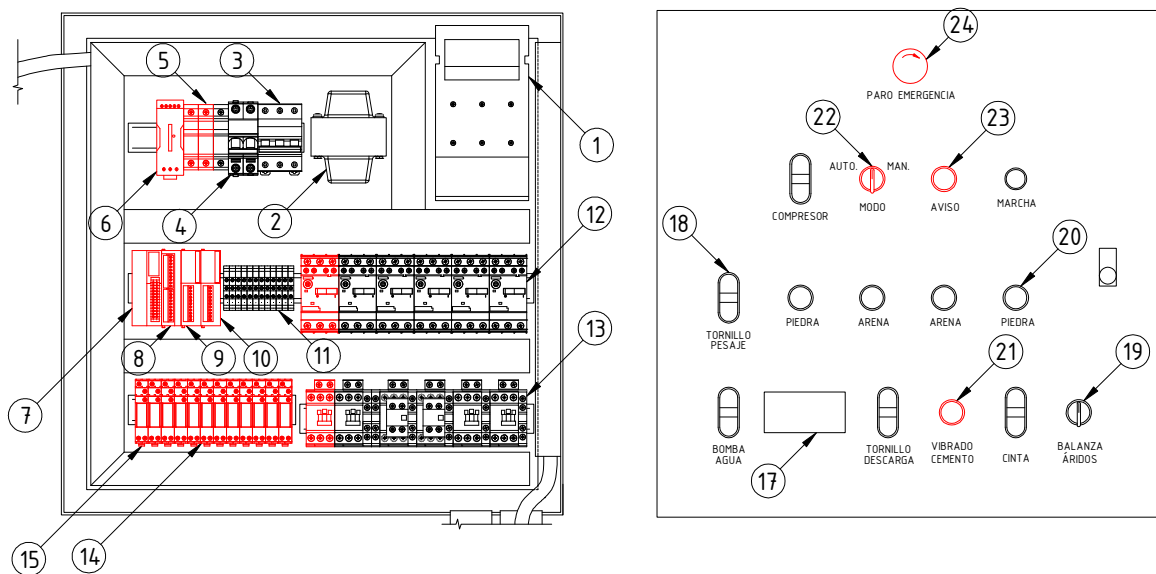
Disposición de elementos en la bandeja y puerta del tablero.
